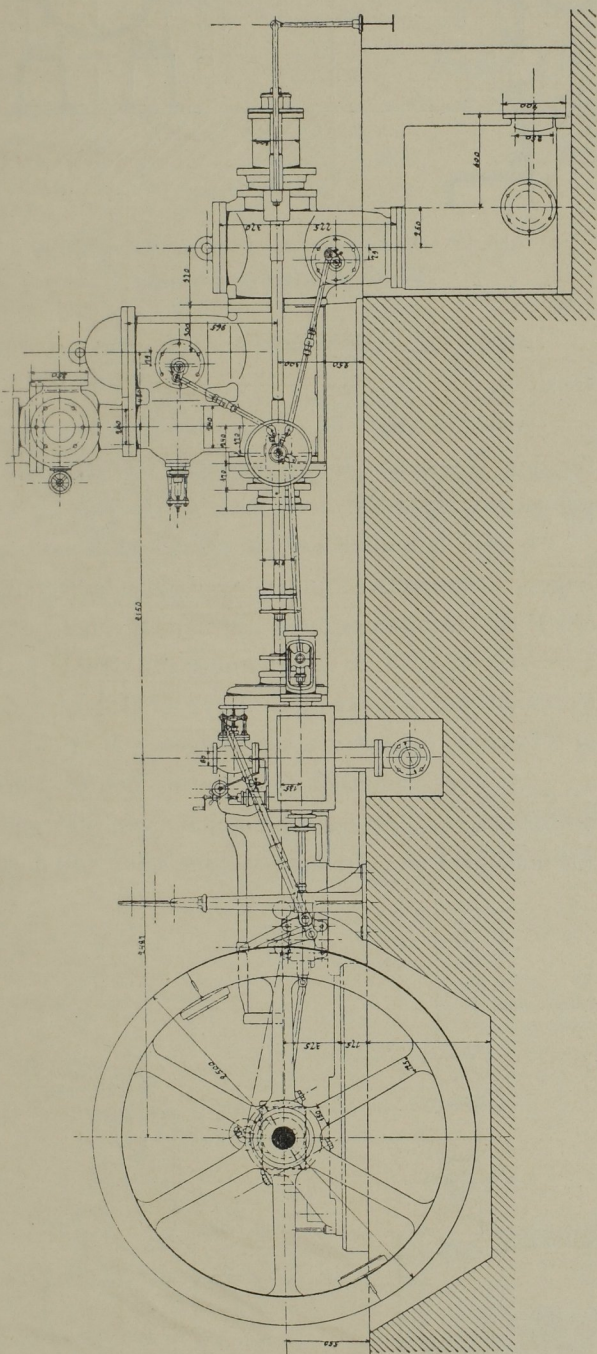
Seitenansicht der Maschine. Masst. 1 : 75.
